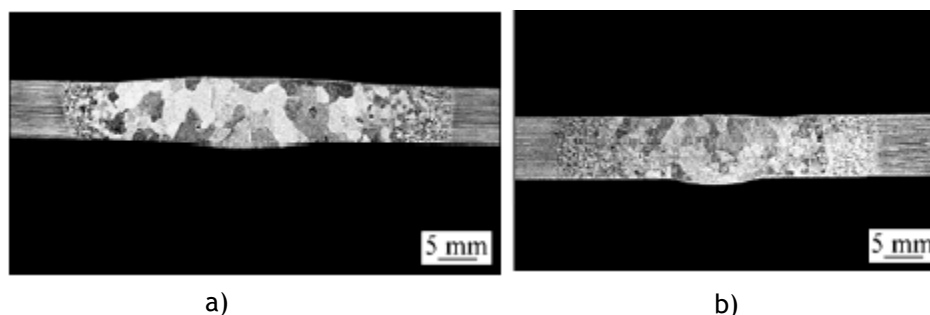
Macroestruturas das juntas de soldadura obtidas por: a) TIG; b) Plasma
